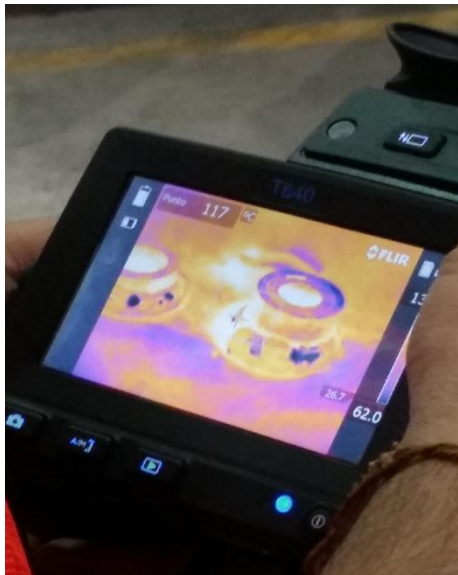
Imagen infrarroja del metal de soldadura de un componente del tanque A1 (30)
